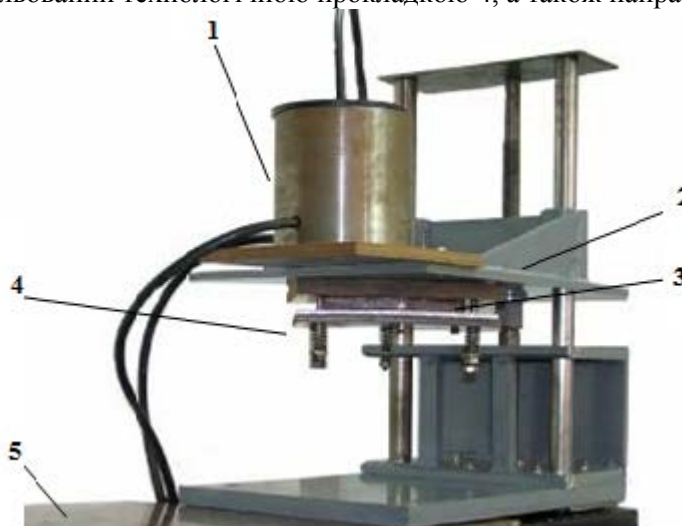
Загальний вигляд магнітно-імпульсної установки: 1 – розрядник, 2 – корпус установки, 3 – індуктор, 4 – супутник, 5 – блок живлення.
